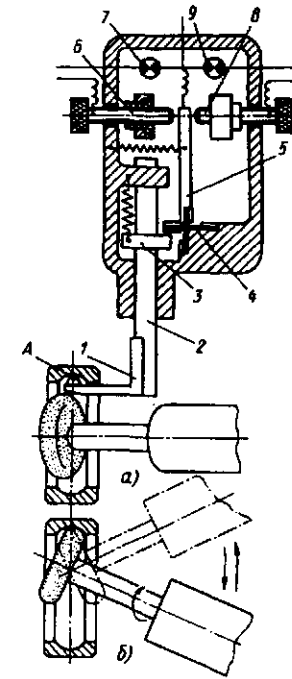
Схема прибора активного контроля при внутреннем шлифовании: а – схема измерения; б – схема шлифования
